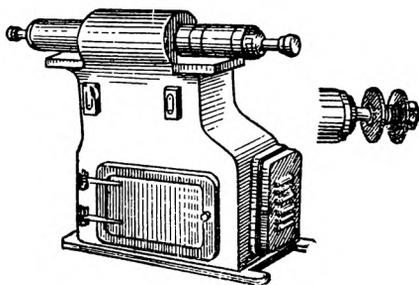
Двухшпindelный двусторонний шлифовально-полировальный станок (тип 385).
